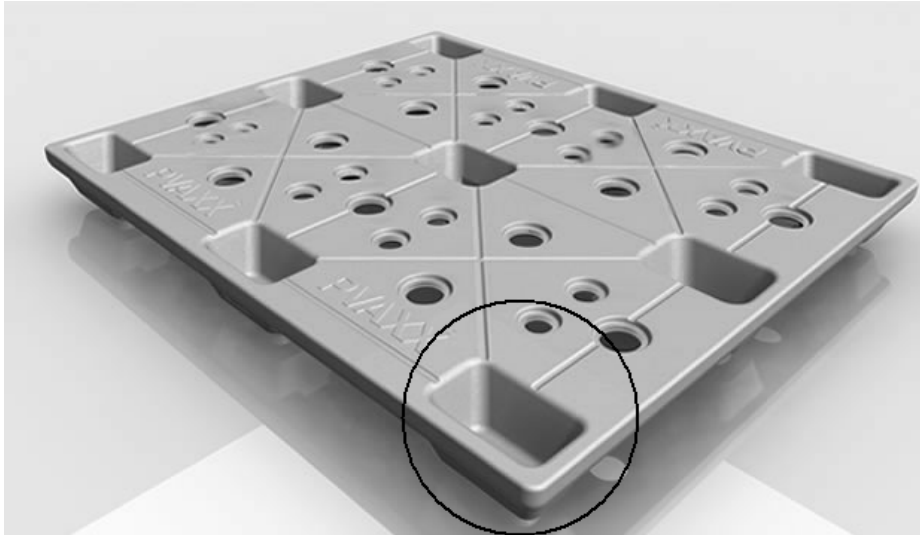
Pieza plástica con columnas permanentes. Imagen tomada de Roto Design Ltd.
